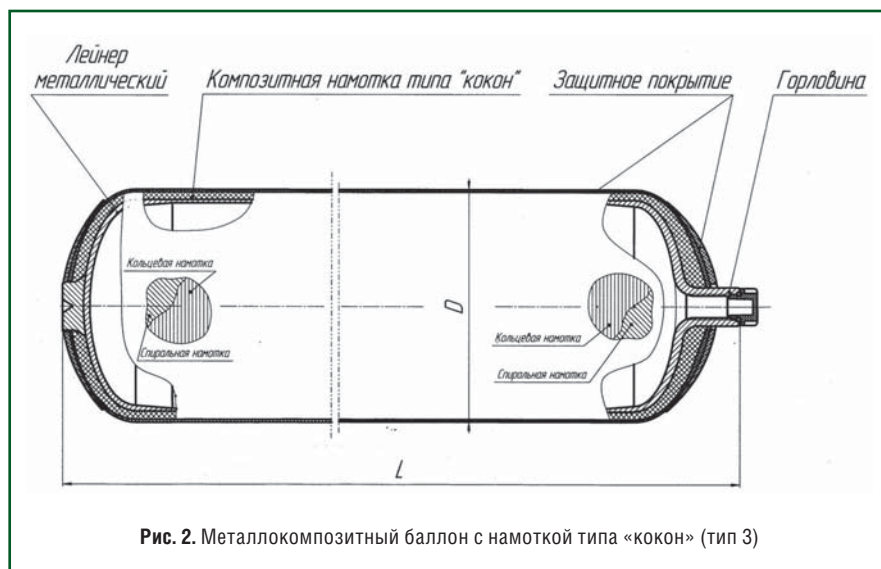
Металлокомпозитный баллон с намоткой типа «кокон» (тип 3)
